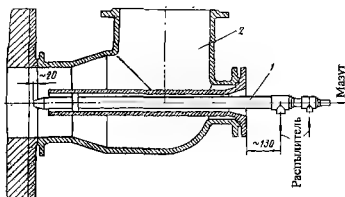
Установка форсунки высокого давления с двойным распыливанием в форсуночной коробке: 1 — форсунка; 2 — форсуночная коробка
